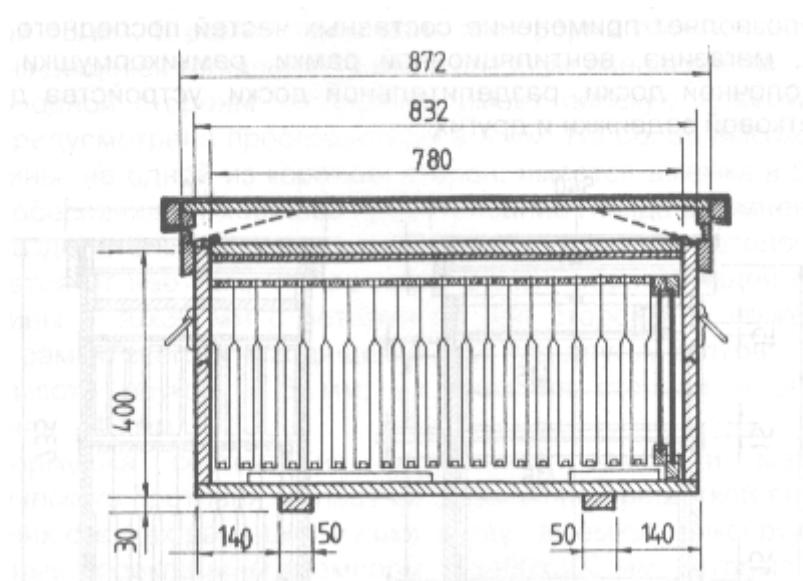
Горизонтальный улей СТАС № 4170/1976 – поперечный разрез
